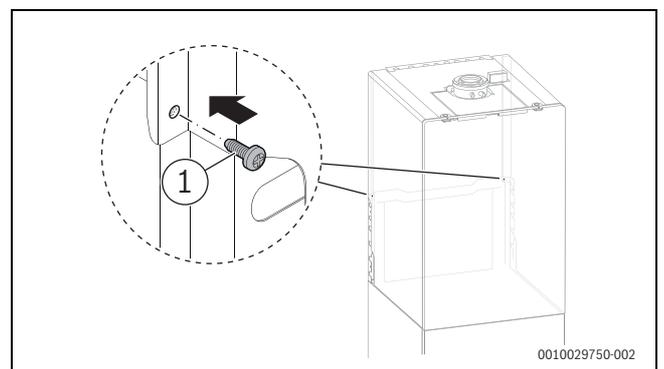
Visser fermement les panneaux latéraux de l'habillage sur les côtés gauche et droit
